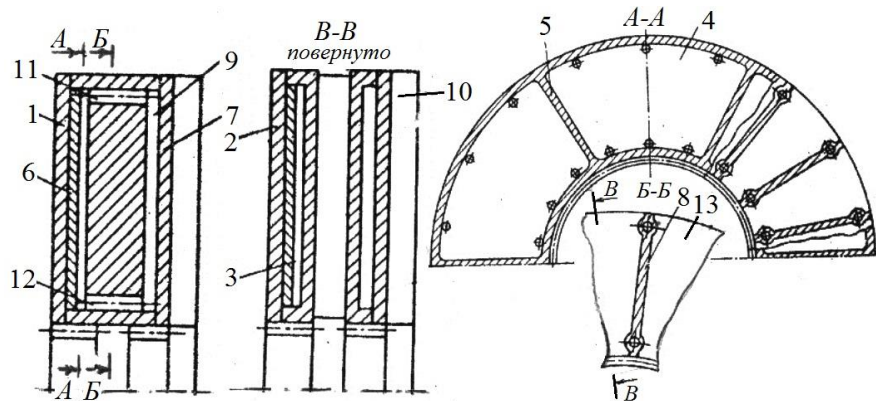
Гальмівний диск: 1, 2 - гальмівний диск з робочою поверхнею; 3, 9 - внутрішні порожнини; 4 - окремі сегменти; 5 - радіальні перегородки; 6 - пористий матеріал; 7 - додаткове порожнисте кільце; 8 - перемичка; 10 - ребра; 11, 12 - наскрізні отвори; 13 - вентиляційні канали
